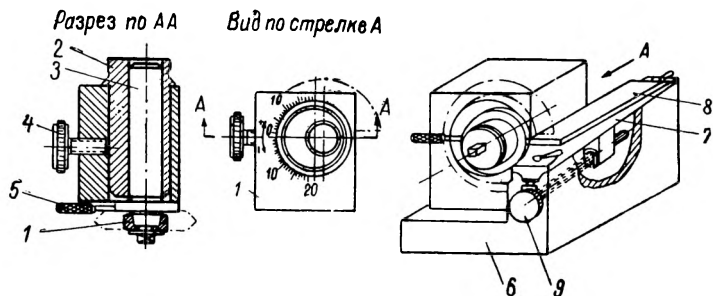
Приспособление для доводки передней грани дискового инструмента
